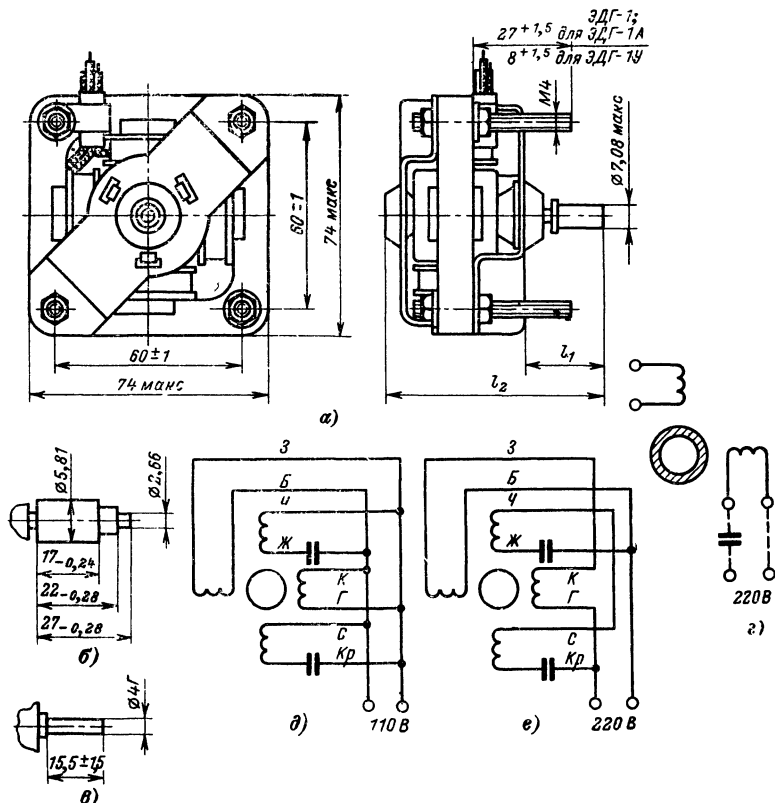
Габаритный чертеж и схемы включения двигателей серии ЭДГ.
